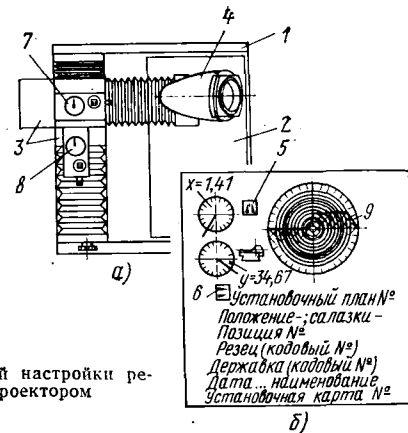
Прибор для размерной настройки режущего инструмента с проектором
